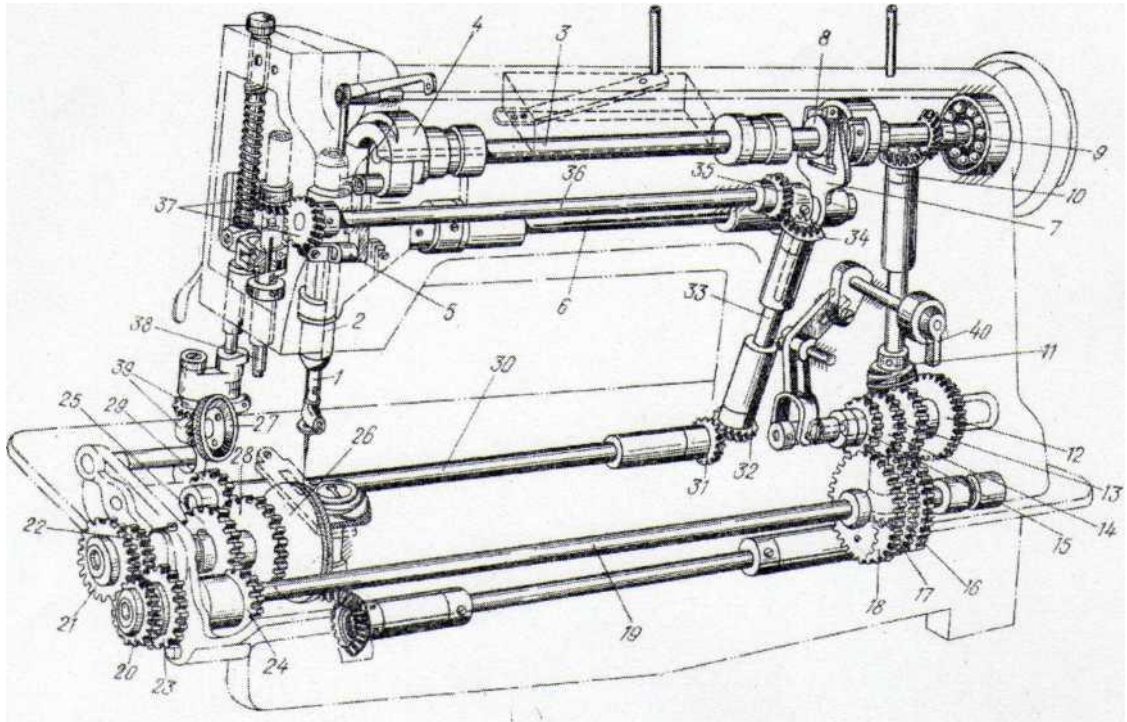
Кінематична схема швейної машини 230 кл.
